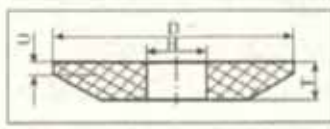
Профиль для заточки (пил), шлицшлифования.
